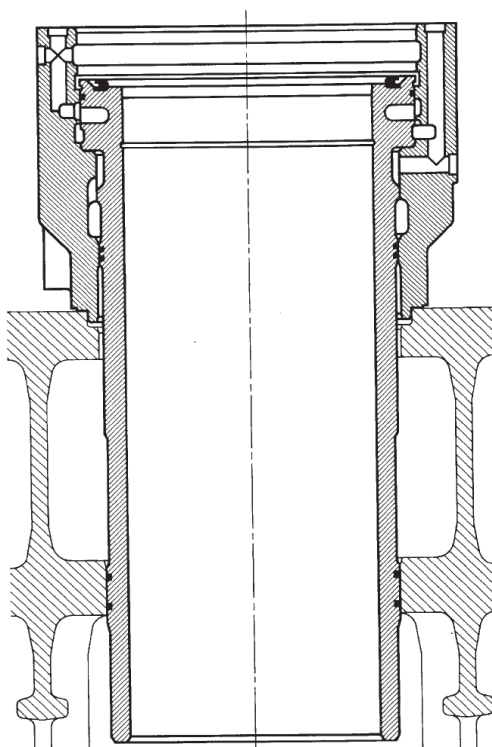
Конструкція втулки робочого циліндру дизеля серії L58/64
